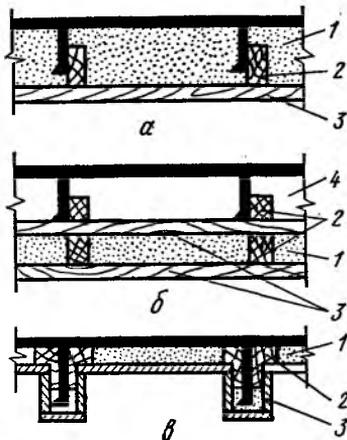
Конструкции судовой изоляции: а — нормальная; б — с воздушной прослойкой; в — с высадками; 1 — изоляционный материал; 2 — деревянный брусок; 3 — деревянная зашивка; 4 — воздушная прослойка.
